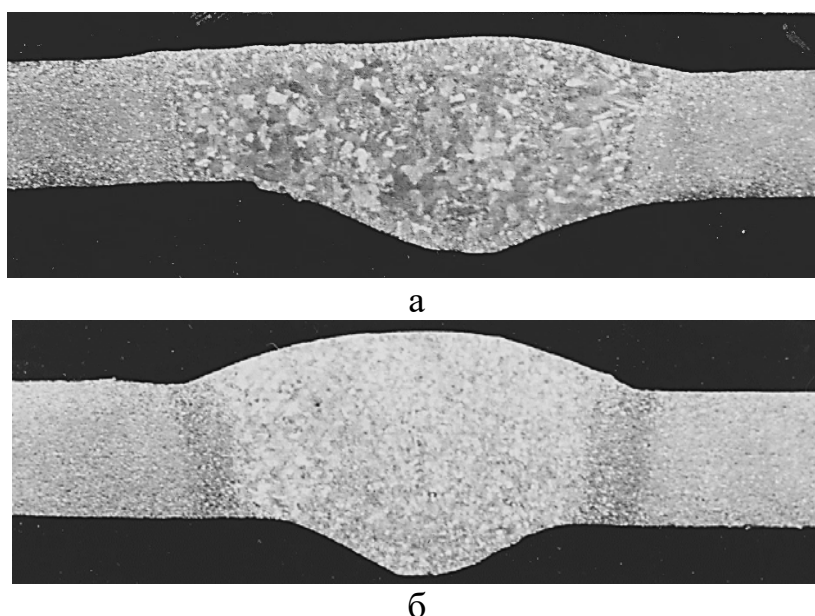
Макроструктура стыковых сварных соединений листов сплава 1565чМ толщиной 3 мм при механизированной однопроводной плазменной сварке с различными присадками: а – СвАМг63; б – СвАМг63+Sc;
